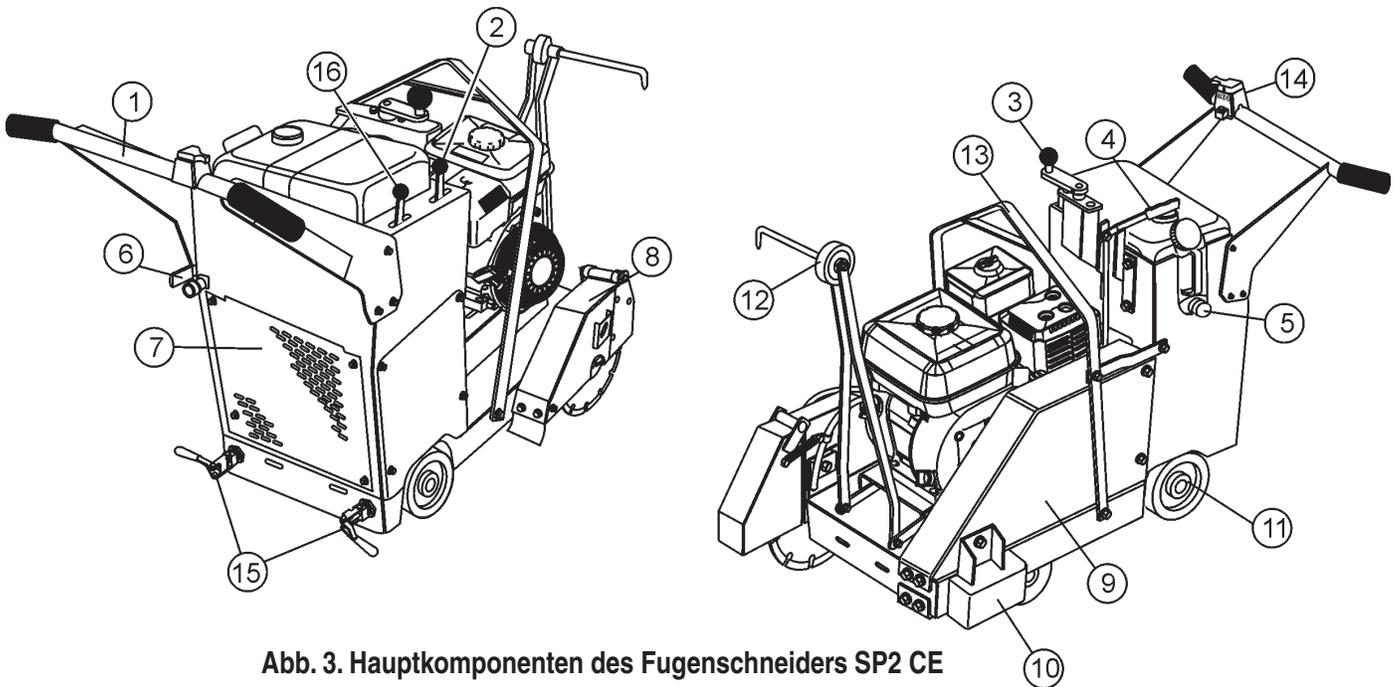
Hauptkomponenten des Fugenschneiders SP2 CE
